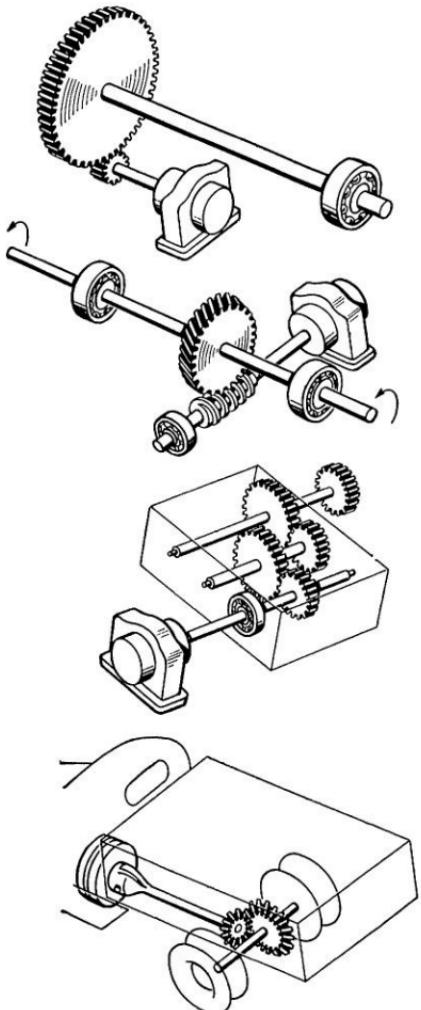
Редукторы и передачи вращения вала электродвигателя
